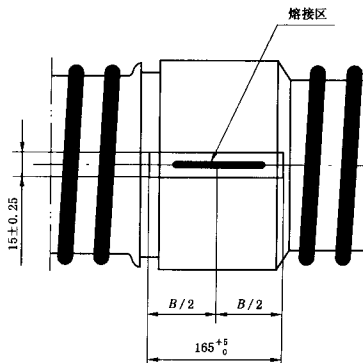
焊缝或熔缝的拉伸强度制备试样的位置和尺寸(单位:mm)
